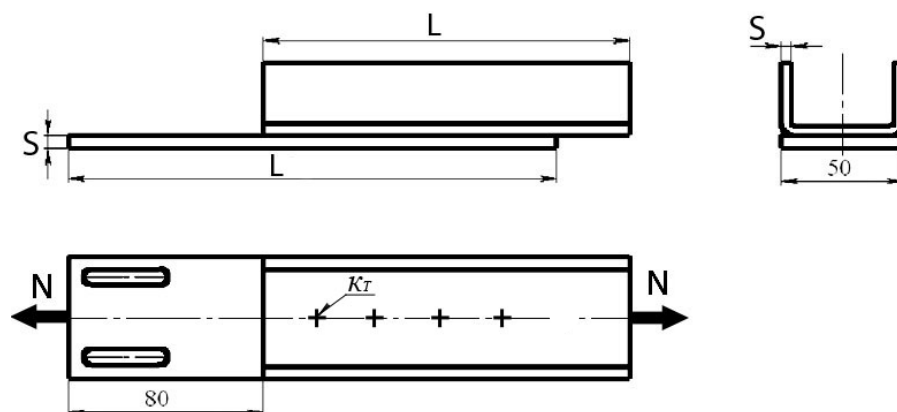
Конструкция, выполняемая контактной точечной сваркой
